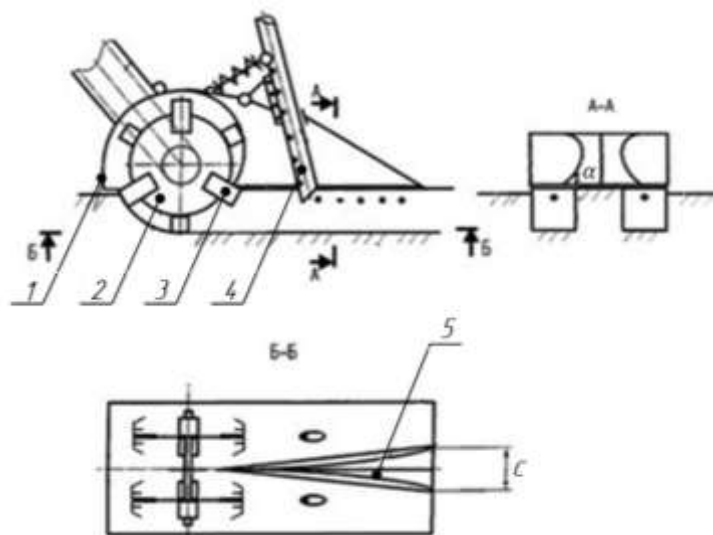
Усовершенствованный фрезерный сошник сеялки СДК-2,8: 1 – кожух фрезерной секции; 2 – фреза; 3 – усовершенствованные L-образные ножи; 4 – семянаправитель; 5 – двусторонний отвал
